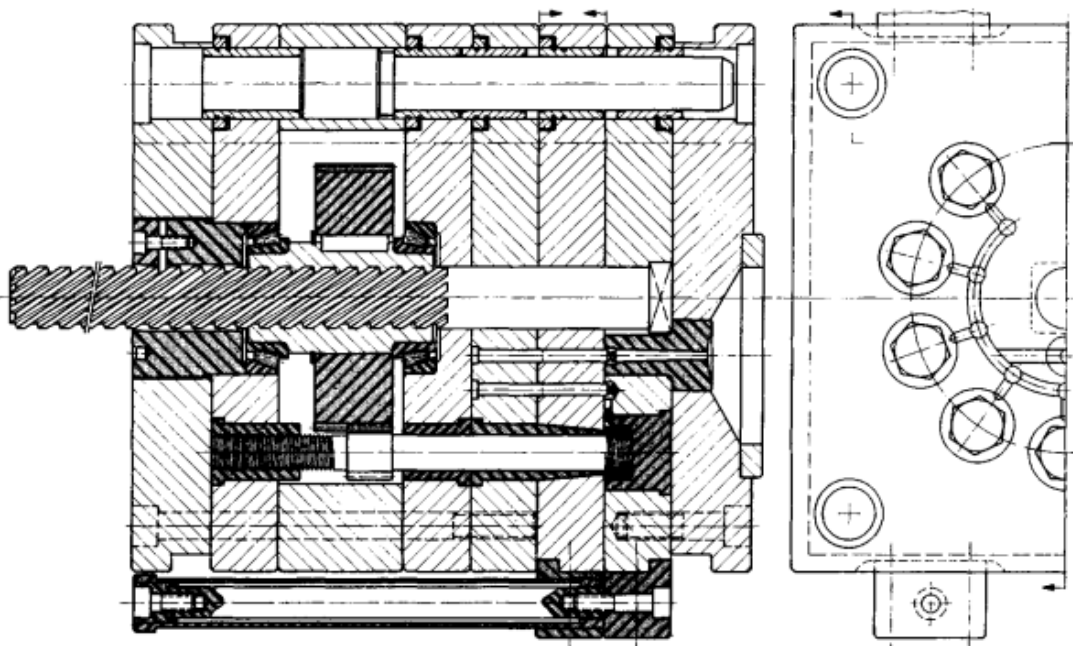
Husillo que gira en el interior del molde, mientras que la tuerca está fija en el travesaño del eyector. Fuente: How to make injection molds [7].
